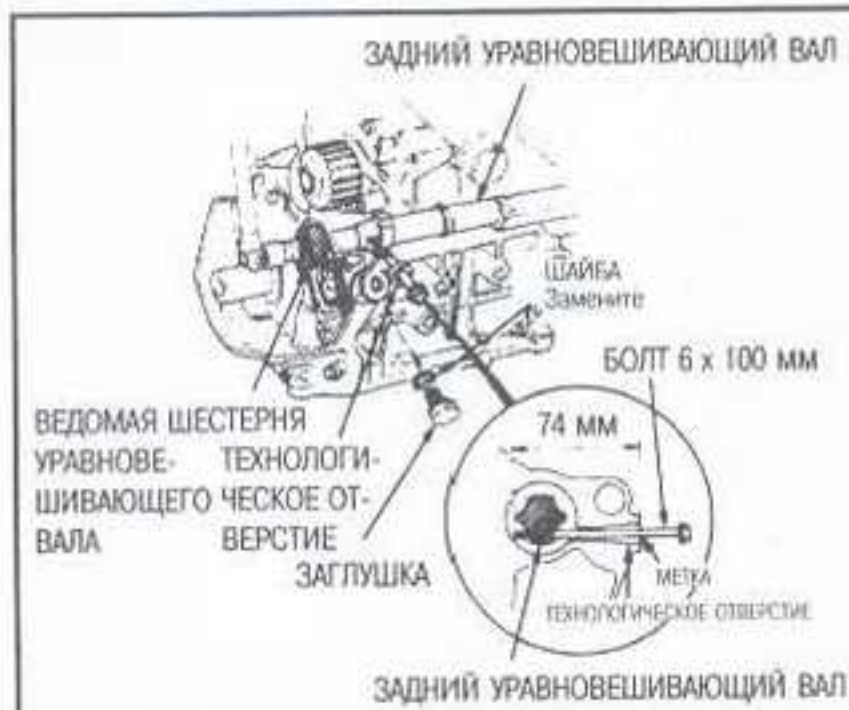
Установка технологического болта - 4-цилиндровые двигатели моделей Odyssey
